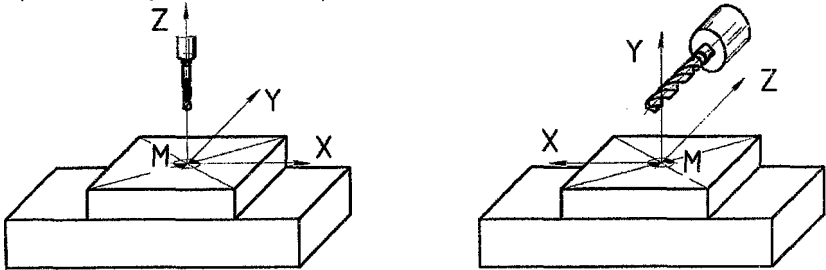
Типовые системы координат фрезерных, сверлильных и расточных станков с ЧПУ
